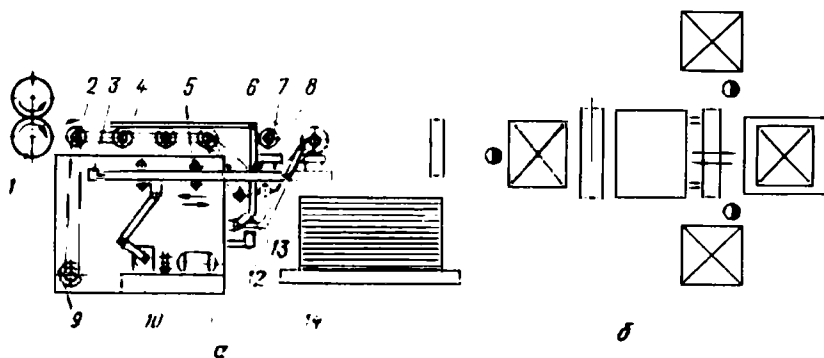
Устройство для механизации сборки пакетов шпона конструкции НПО «Научфанпром»
